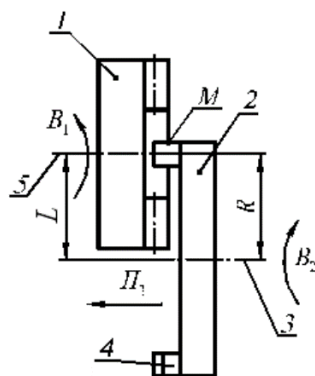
Схема с параллельными осями инструмента и заготовки
